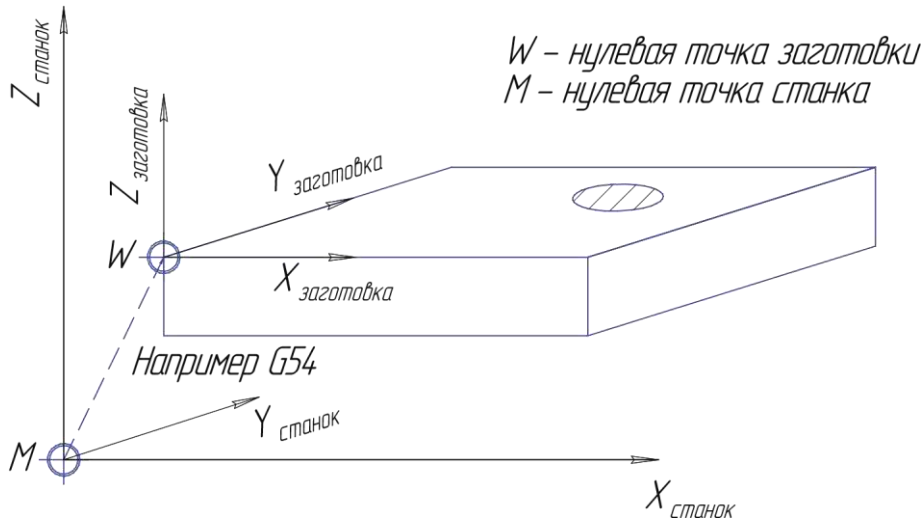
Смещение нуля M станка в точку нуля W заготовки
